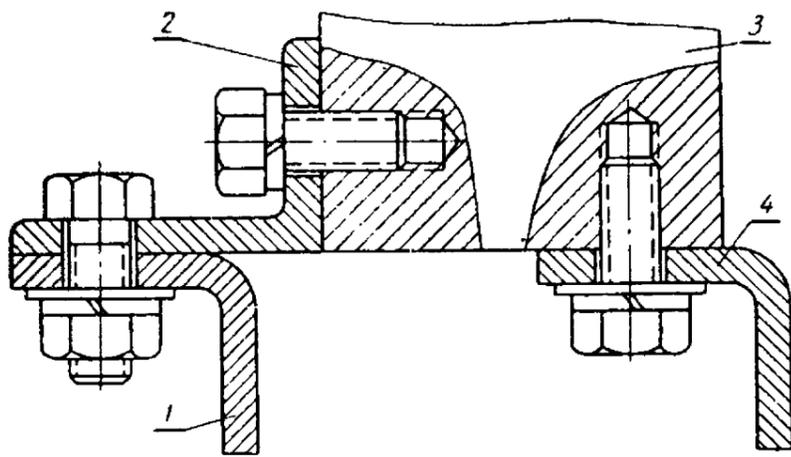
Схема навешивания коробки ведомого шкива клиноременной передачи:
